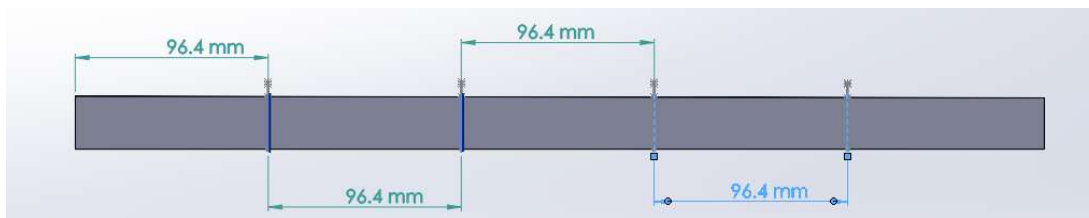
Croqui da distribuição de termopar na placa de teste. Ilustração: Autor.
